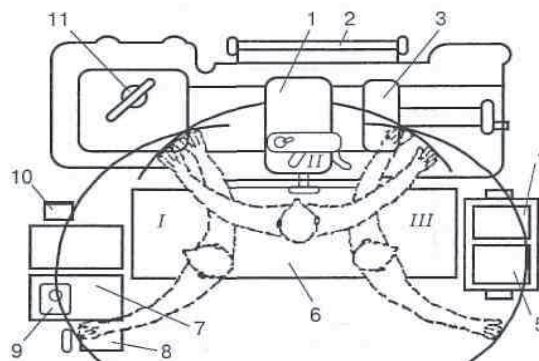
Організація робочого місця токаря: I – зона обслуговування; II – робоча зона; III - зона розміщення заготовок та деталей; 1 – верстат; 2 – екран; 3 – лоток; 4 – столик; 5 – тара; 6 – ґрати; 7 – тумбочка; 8 – стілець; 9 – пульт зв'язку; 10 – урна для сміття; 11 – планшет для креслень.
